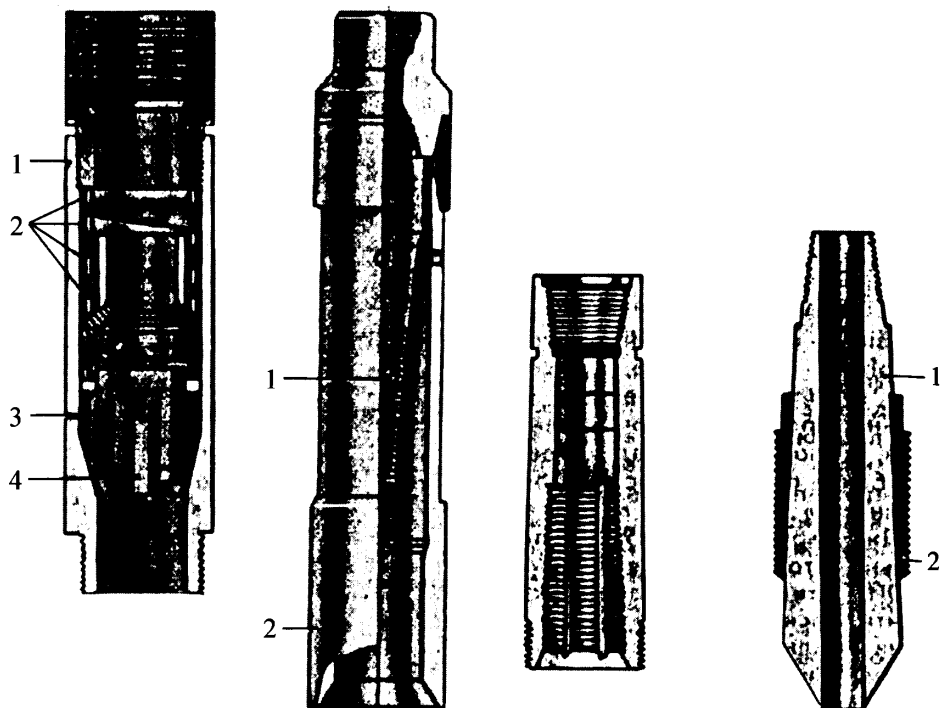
Ловитель: 1 – корпус; 2 – плоская спиральная пружина; 3 – плашка; 4 – шпонка
